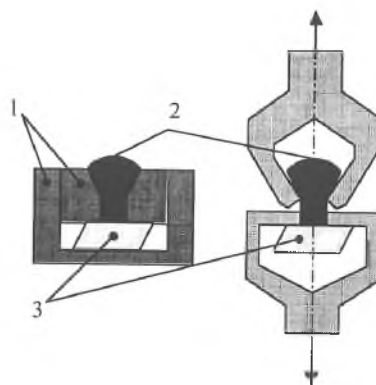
Схема наплавки металла-припоя на кристалл алмаза и разрывных испытаний прочности контакта алмаз-металл: 1 – графит; 2 – металл; 3 – кристалл алмаза.
